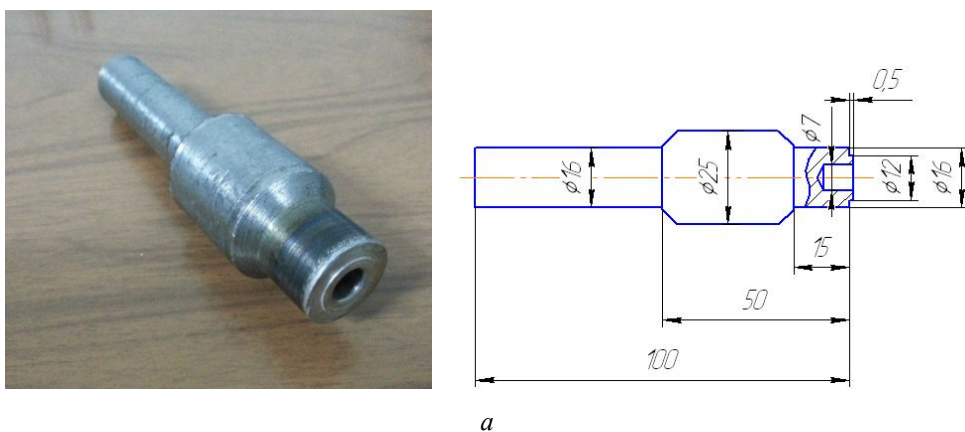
Внешний вид и эскиз инструмента (см. также с. 51):
